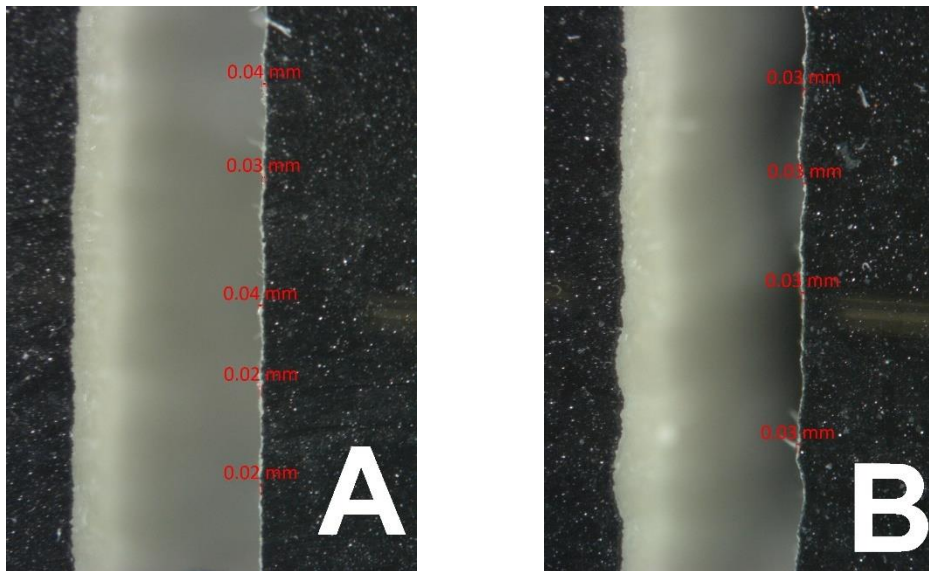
Porovnání delaminované povrchové úpravy materiálu PVC-U s rozdílnou povrchovou úpravou
